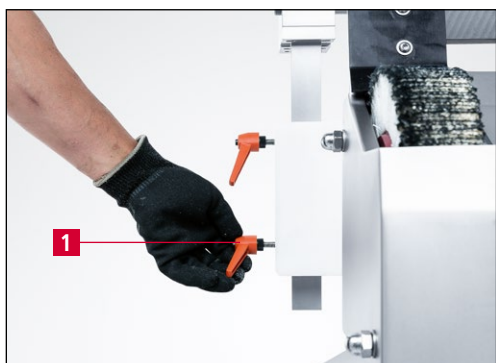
Регулировка ножа в центре шлифовального круга
